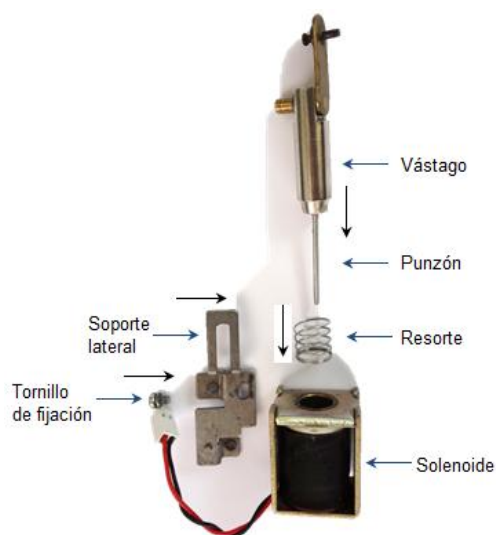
Acondicionamiento mecánico del conjunto solenoide – punzón
